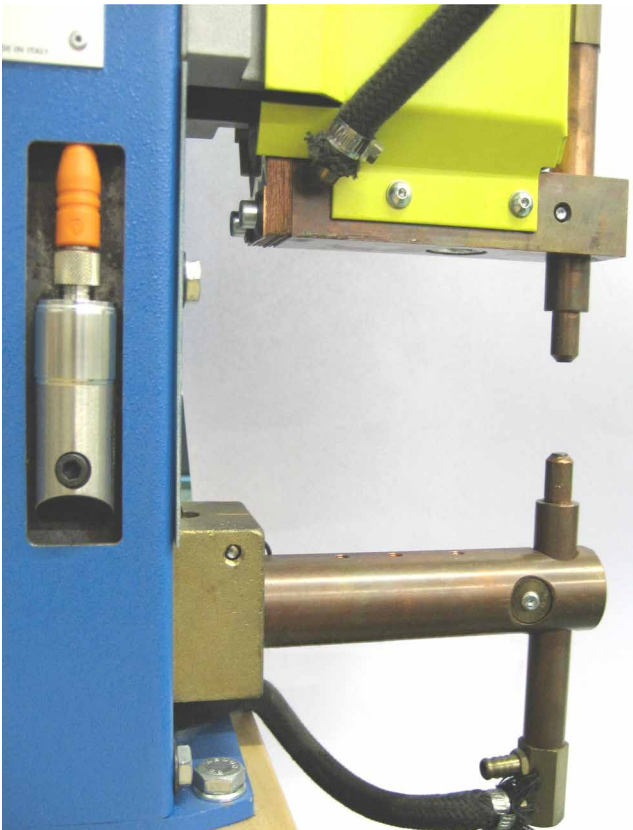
Indirekte Elektrodenkraftmessung an einer Punktschweissmaschine
